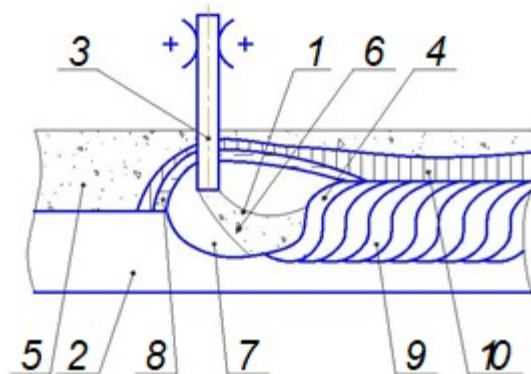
Автоматическая сварка под слоем флюса
